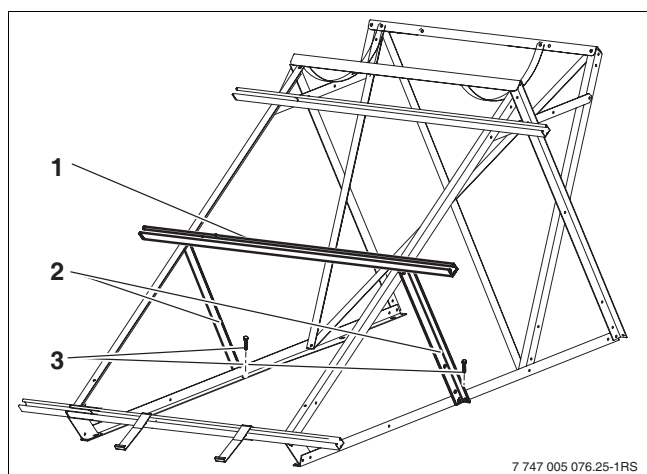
Apoyos adicionales para sistema de cubierta plana (aquí sistema de 150/200 l)
